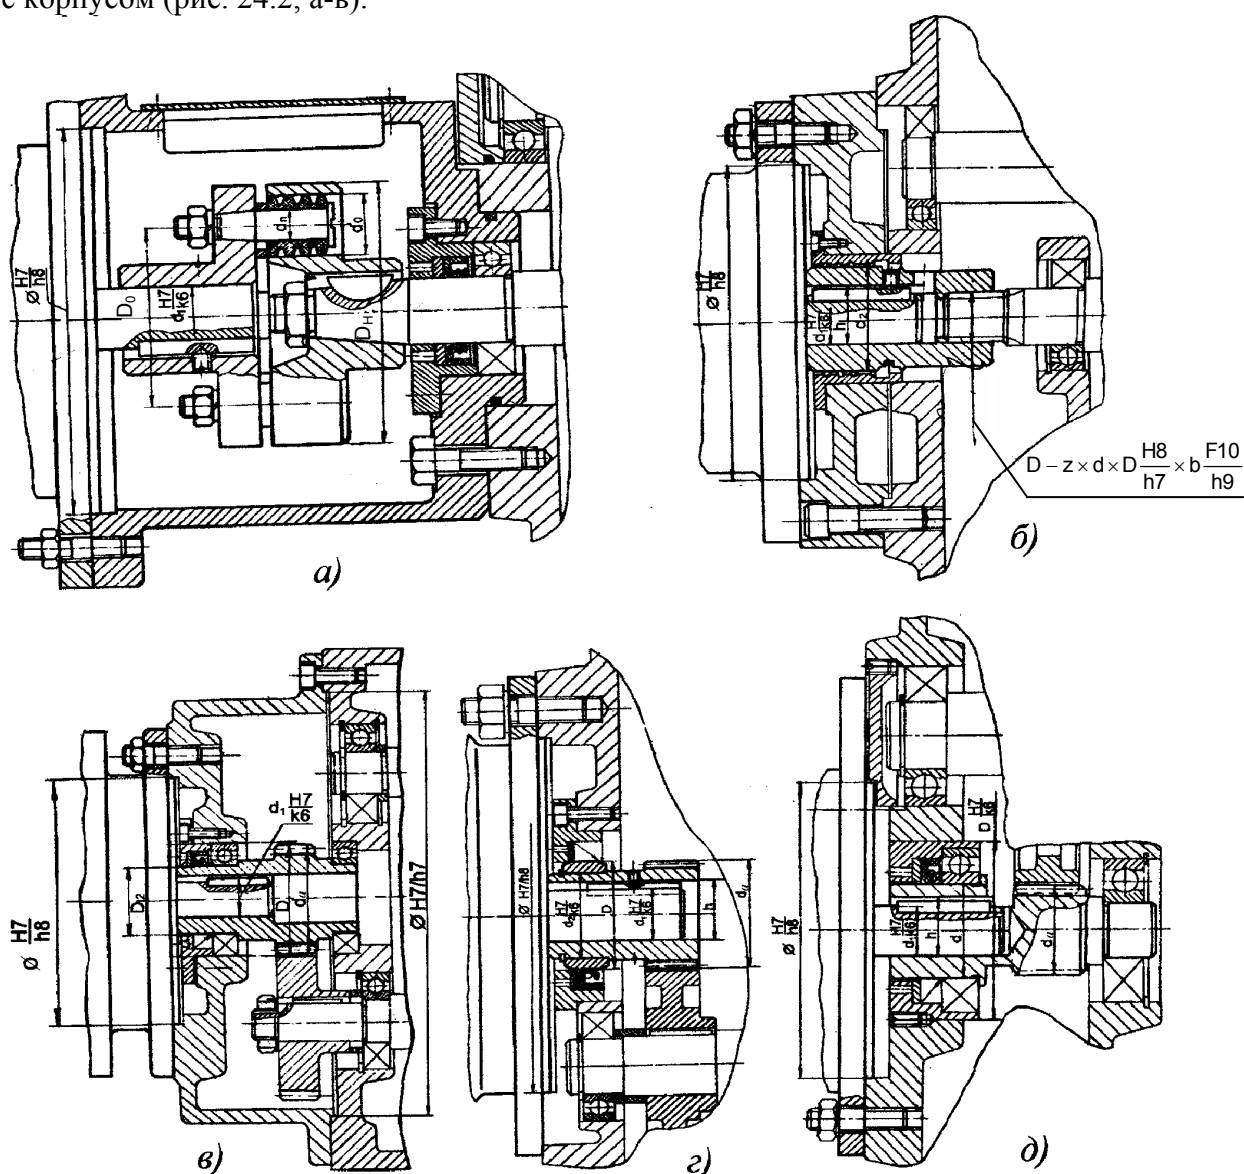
Варианты конструирования мест соединения корпуса коробки и фланцем электродвигателя
